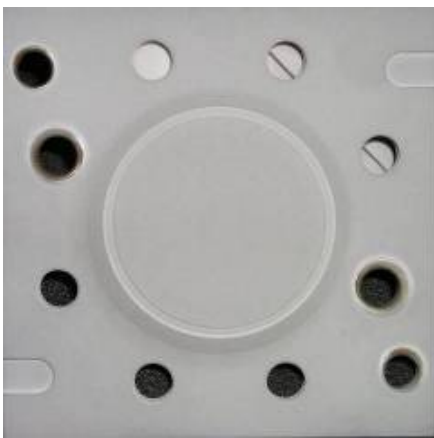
Beschichteter Rahmen mit eingeschweißtem Substrat
